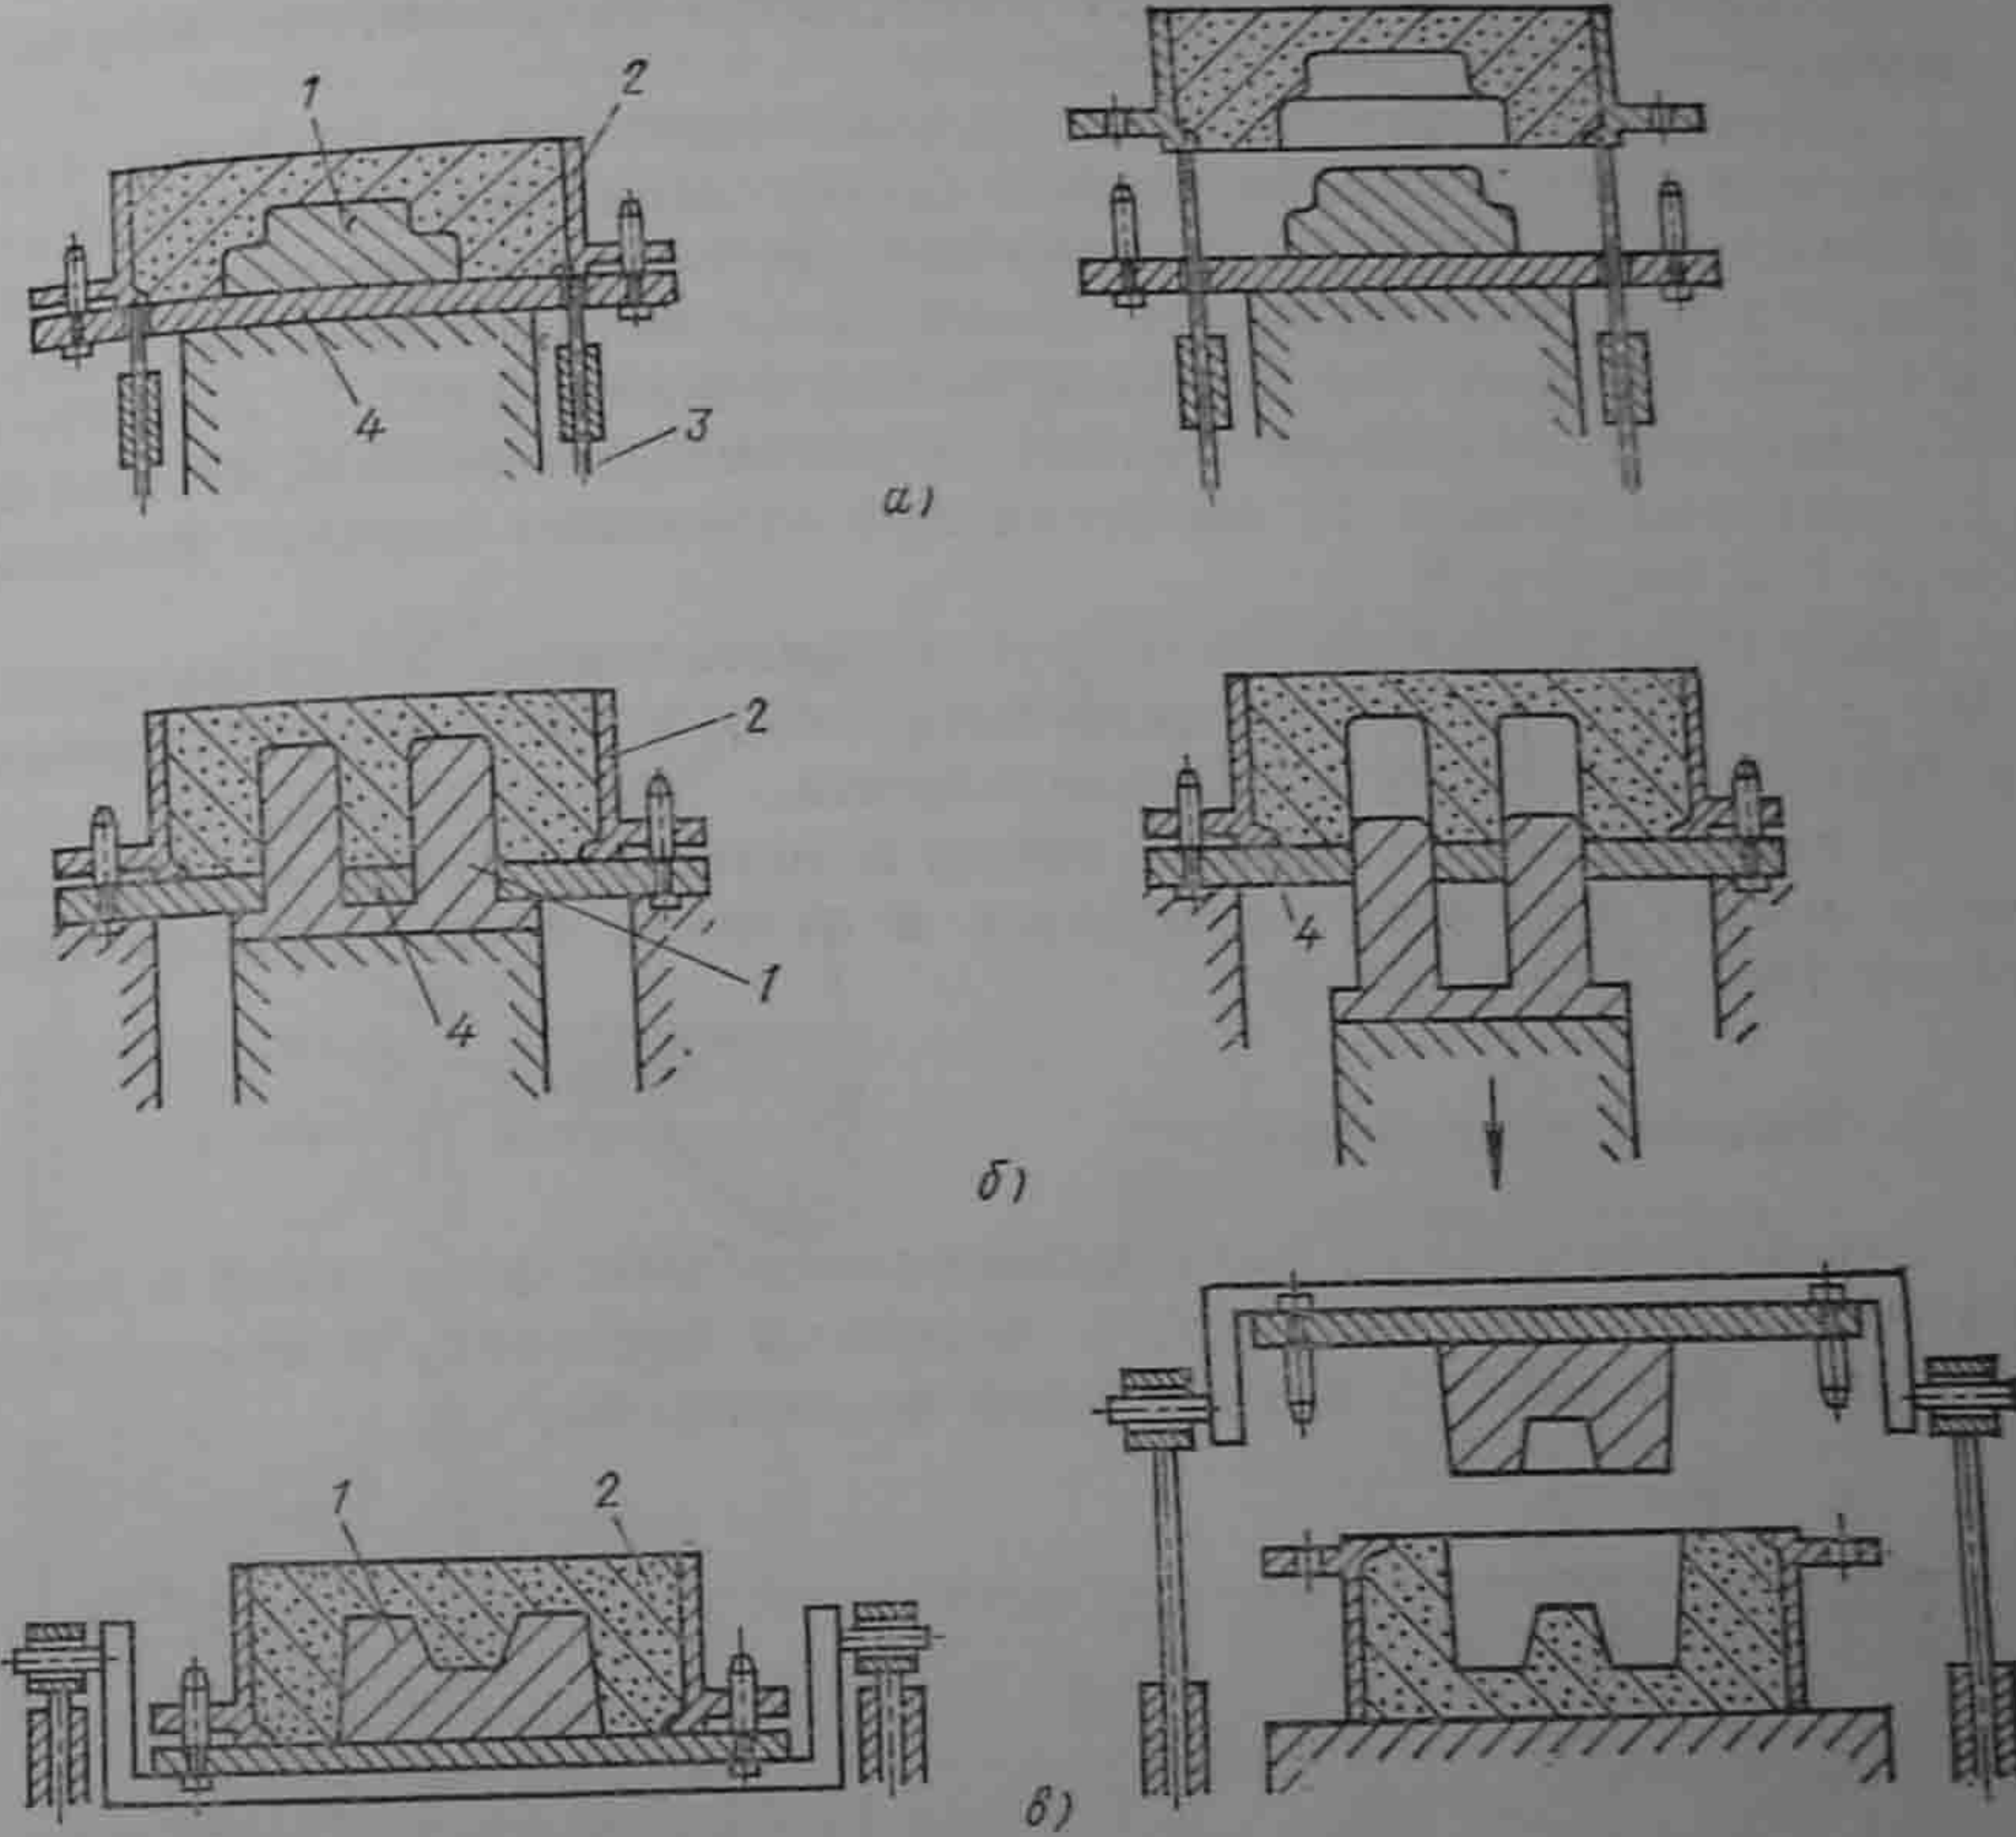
Способы удаления модели из формы: а — штифтовым подъемом опоки; б — через протяжную плиту вниз; в — поворотной плитой
